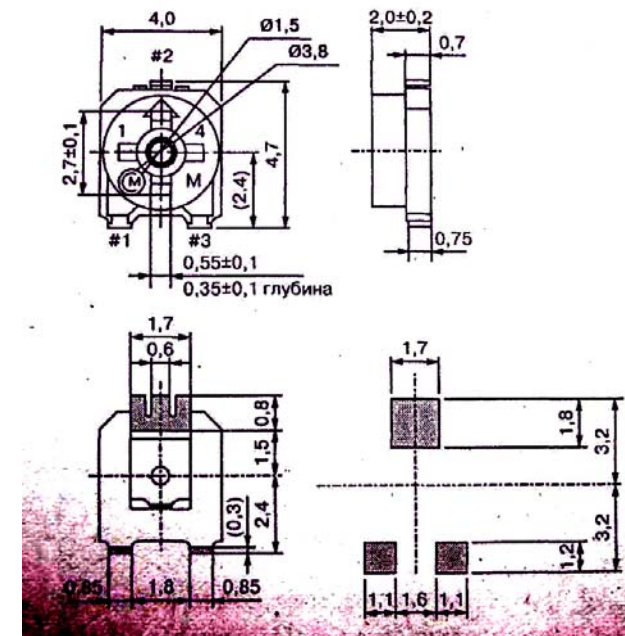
Общий вид, конструкция, габаритные и присоединительные размеры керметного резистора серии RVG4M58
